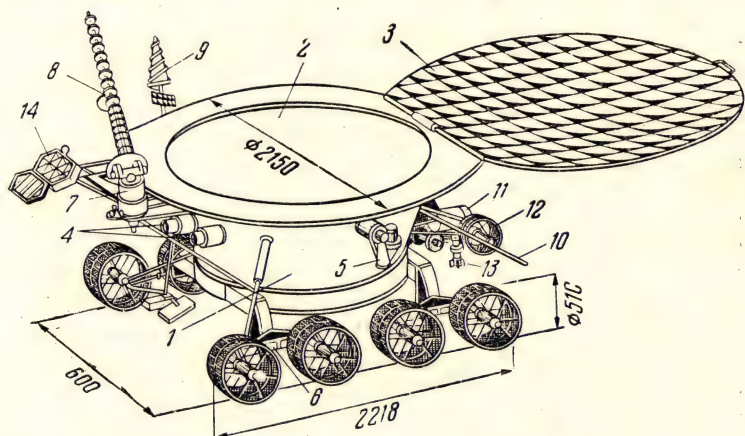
Схематический рисунок, показывающий устройство аппарата «Луноход-1»: 1 — герметичный приборный отсек; 2 — радиатор-охладитель; 3 — солнечная батарея; 4 — илюминаторы для телевизионных камер; 5 — фототелекамеры; 6 — блок колес шасси; 7 — привод остронаправленной антенны; 8 — остронаправленная антенна; 9 — малонаправленная антенна; 10 — штыревая антенна; 11 — изотопный источник тепловой энергии; 12 — девятое колесо; 13 — прибор для определения физико-механических свойств грунта; 14 — оптический уголкового отражатель.
